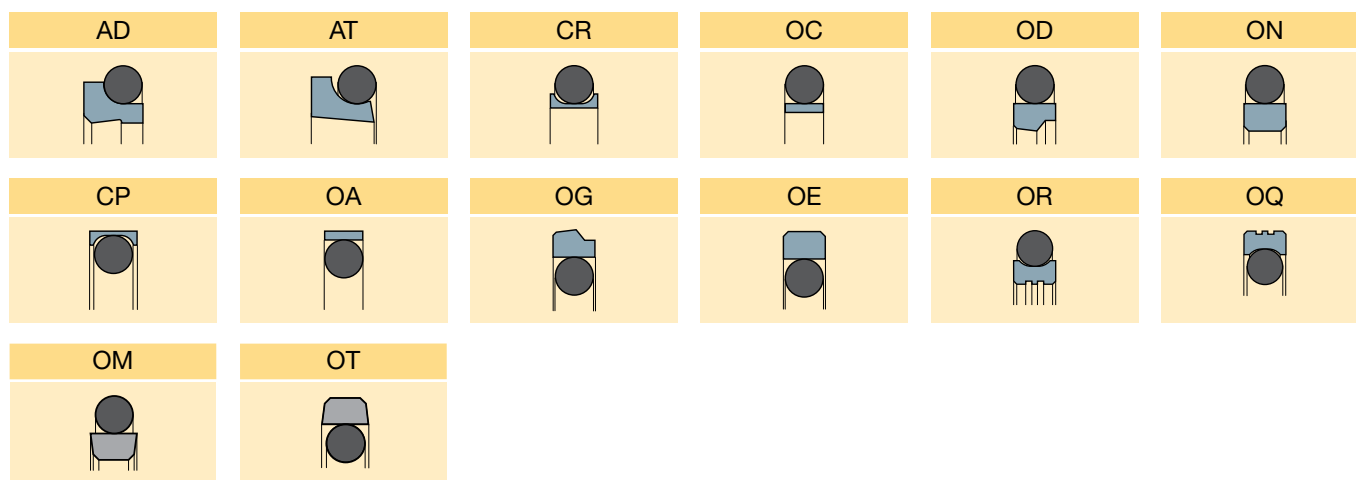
Обзор профилей уплотнителей Slipper Seal®
